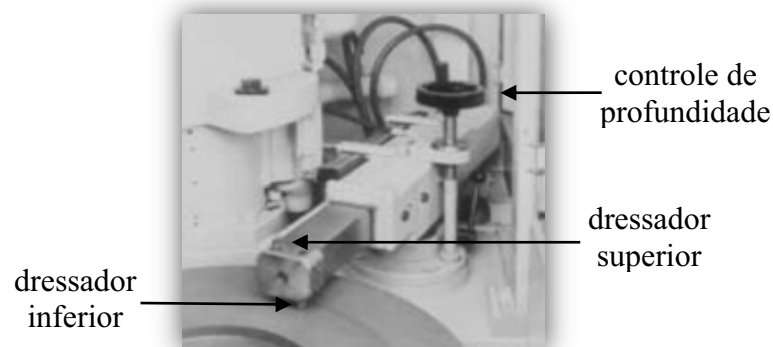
Dispositivo de dressagem dos discos inferior e superior de uma brunidora plana (STÄHLI, 2000 - modificado).
